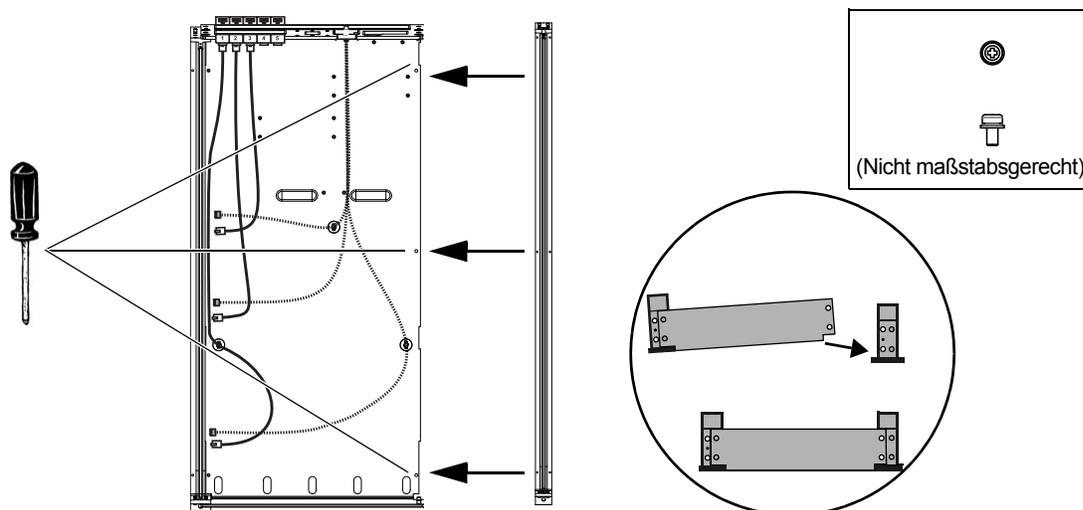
Befestigen der äußeren Seitenwand an der Chassis-Bodenplatte, Draufsicht (links) und Frontalansicht (rechts unten)
